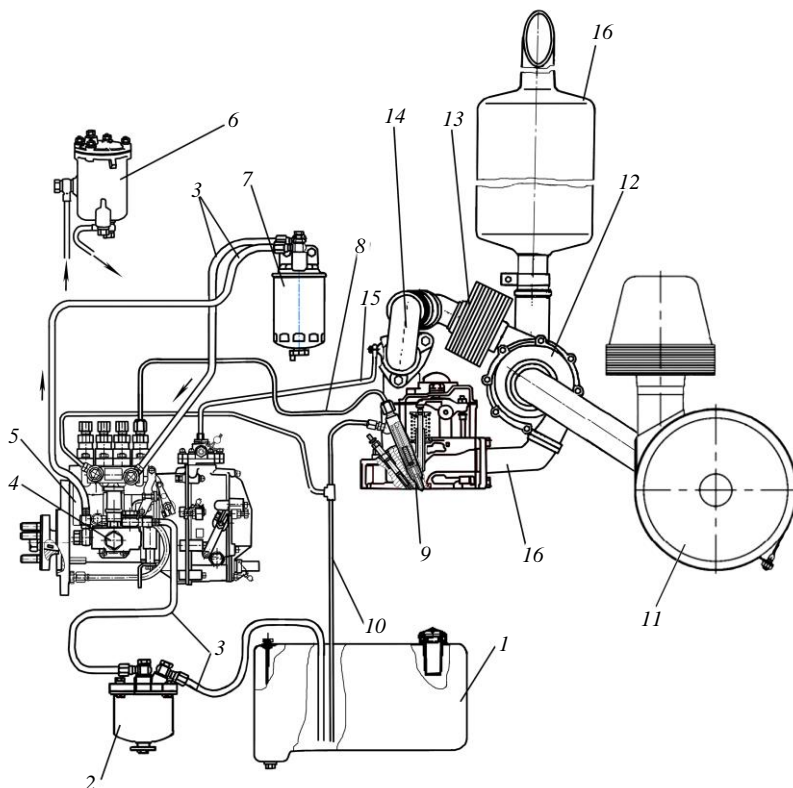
Схема системы питания дизельного двигателя: 1 – топливный бак; 2 – фильтр грубой очистки топлива; 3 – топливные трубки низкого давления; 4 – топливоподкачивающий насос; 5 – топливный насос высокого давления; 6 – фильтр тонкой очистки топлива (со сменным фильтрующим элементом); 7 – фильтр тонкой очистки топлива (неразборный); 8 – топливопроводы высокого давления; 9 – форсунка; 10 – трубка отвода топлива в бак; 11 – воздухоочиститель; 12 – турбокомпрессор; 13 – охладитель надвучного воздуха; 14 – впускной коллектор; 15 – трубка пневмокоректора; 16 – глушитель
